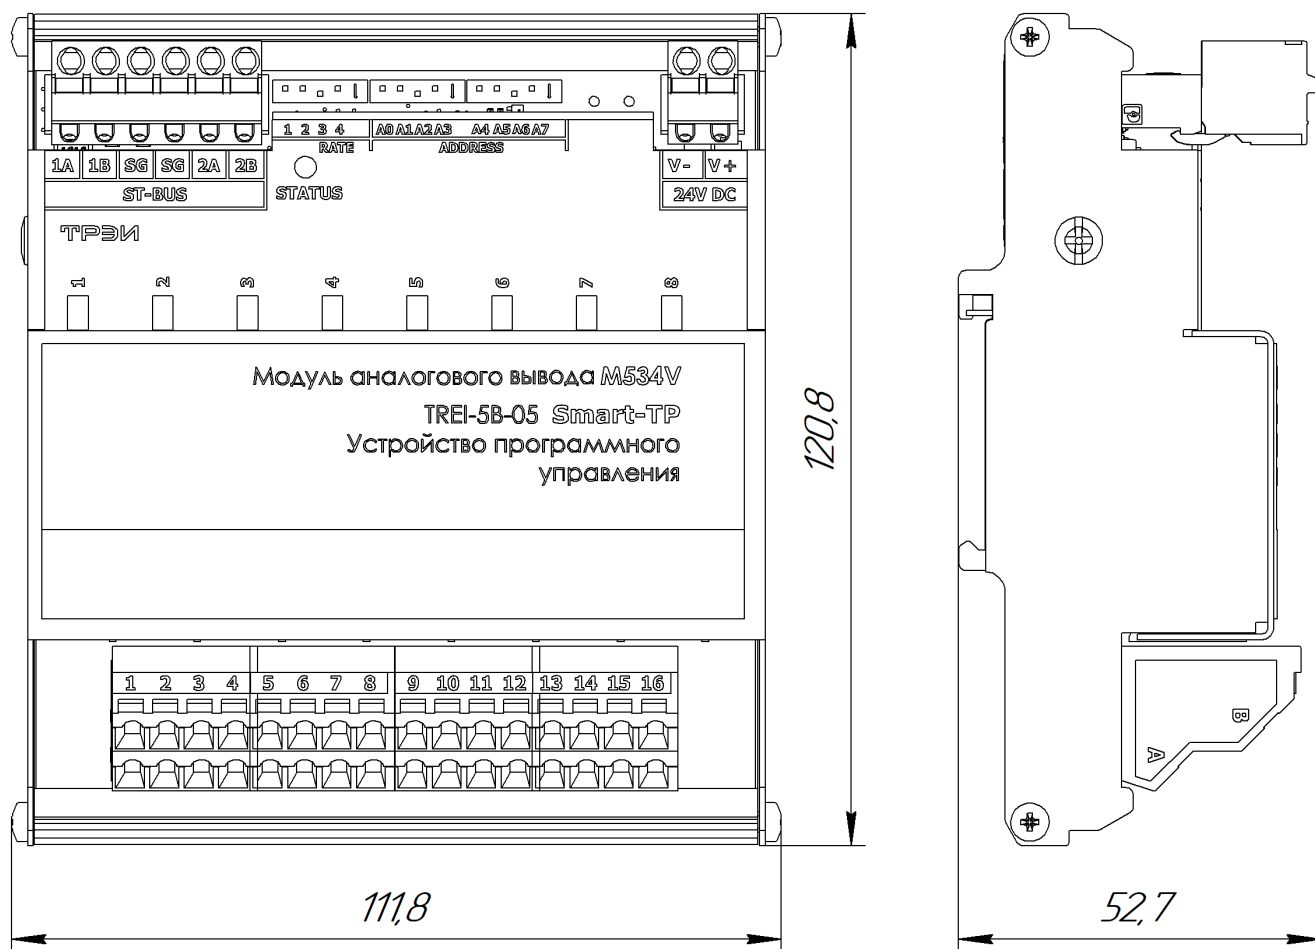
Чертеж общего вида M534V с указанием габаритных и присоединительных размеров
